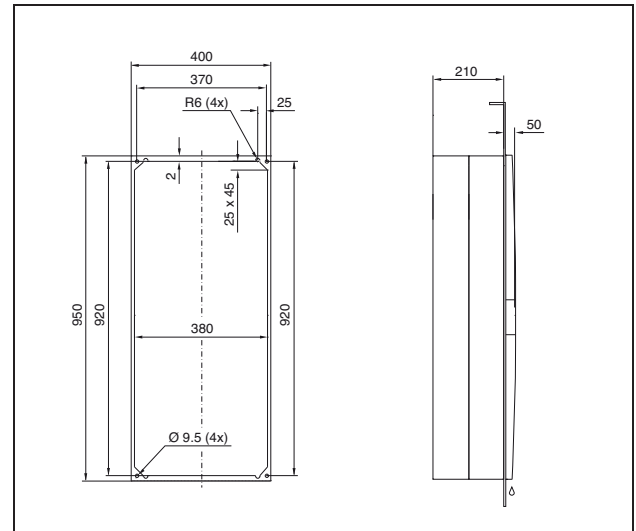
3304.xxx, 3305.xxx komplett inbyggnad
